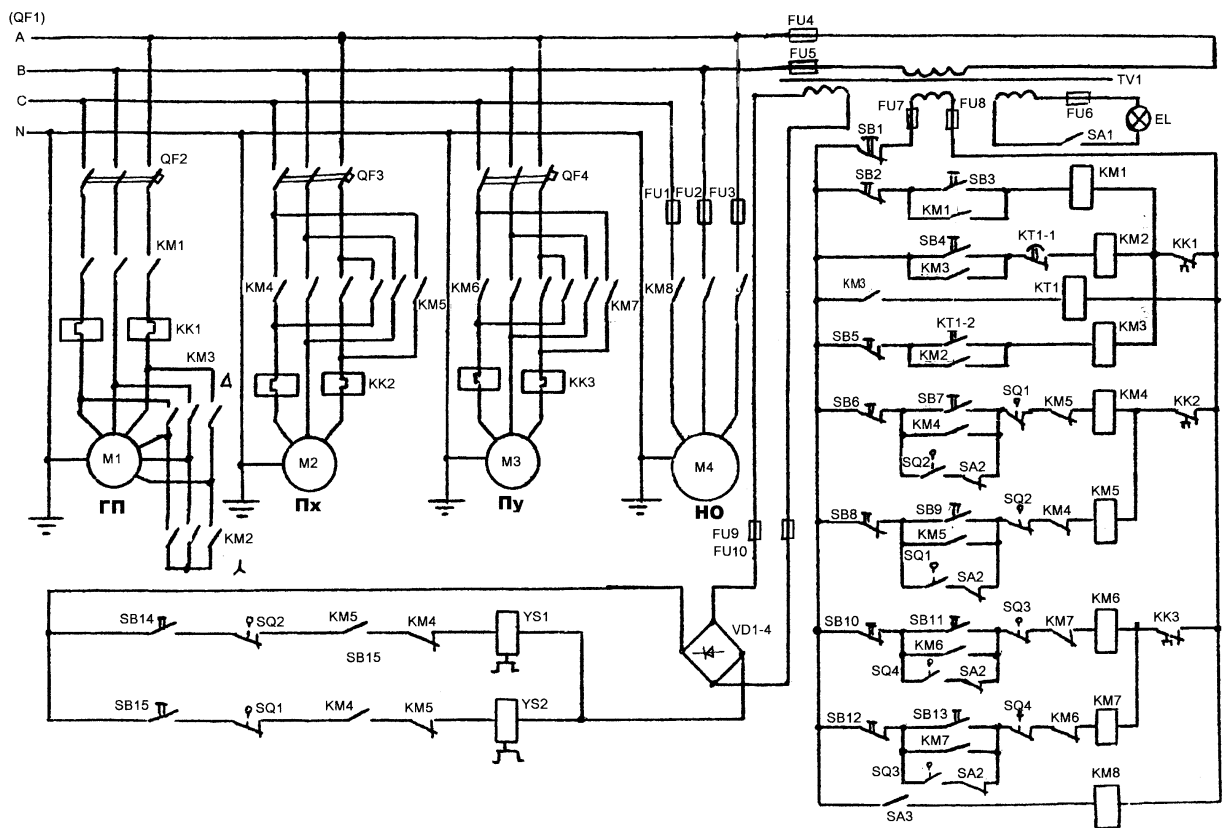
Схема електрична принципова фрезерного верстату 6А59
